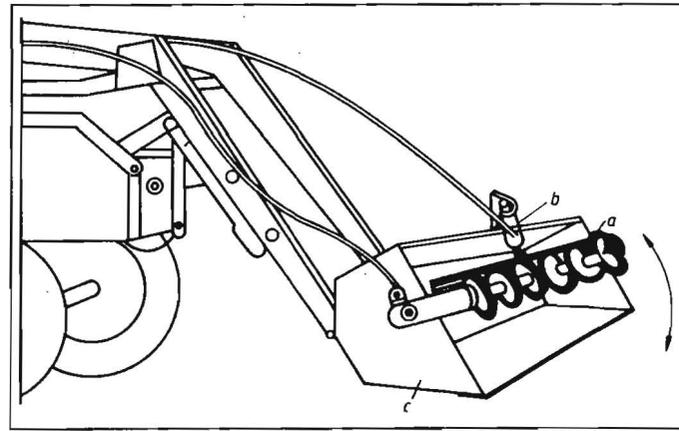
Schaufel mit innenliegender Fräse (nach [5]);
